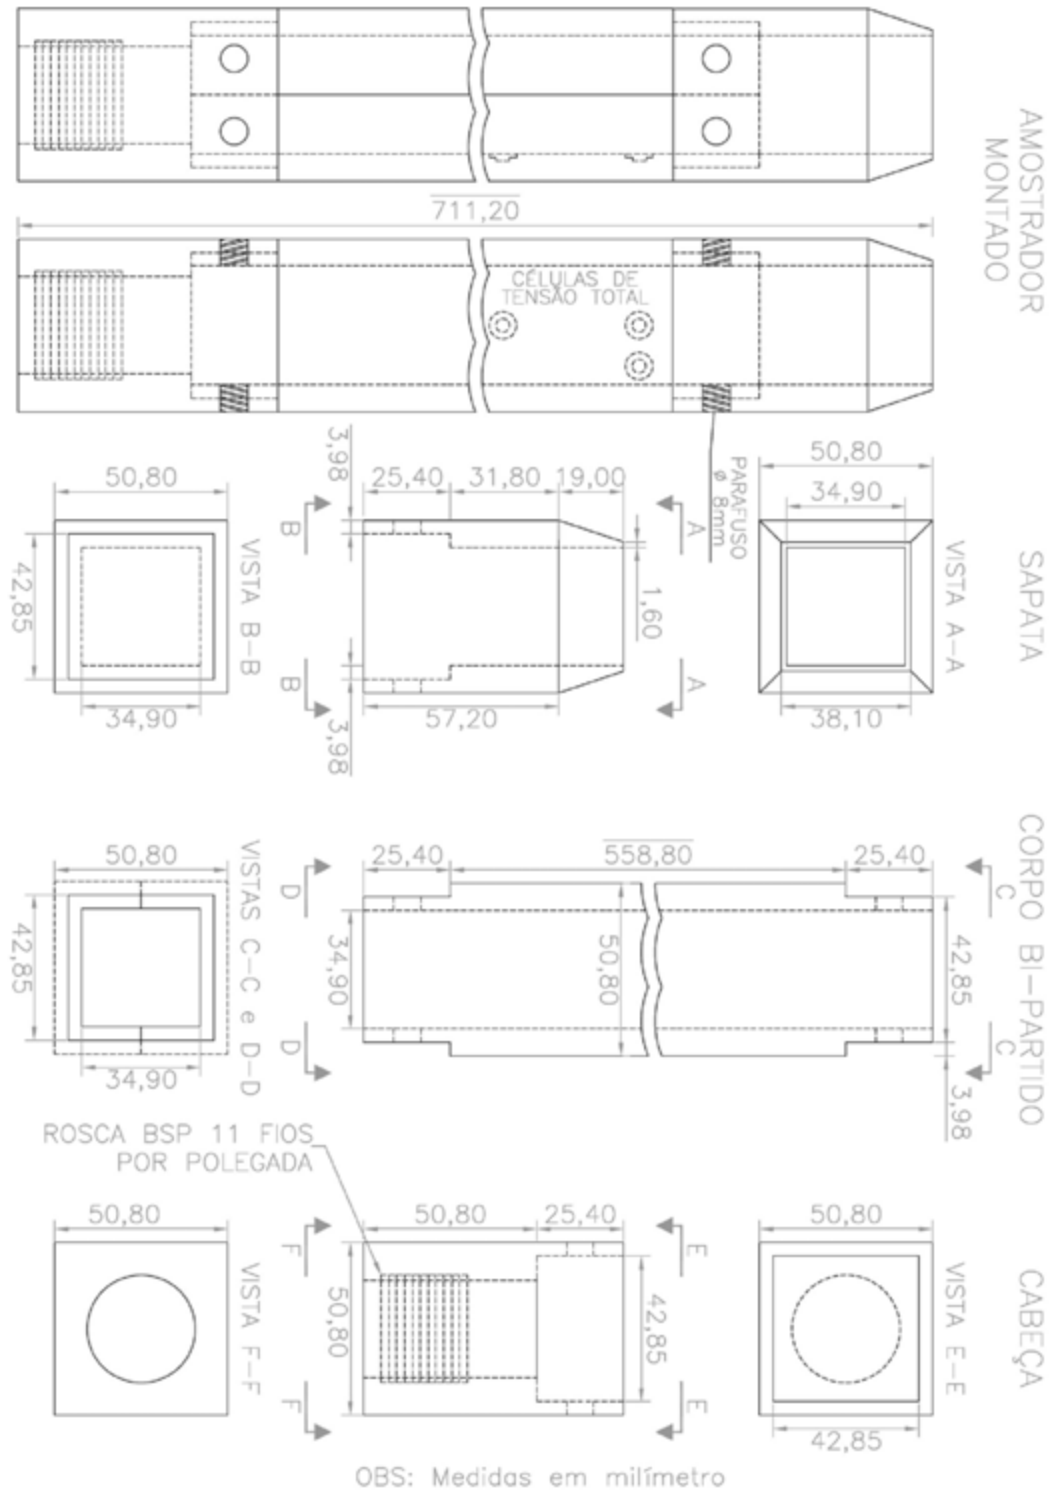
Projeto do novo amostrador instrumentado – Dimensões em milímetro.
